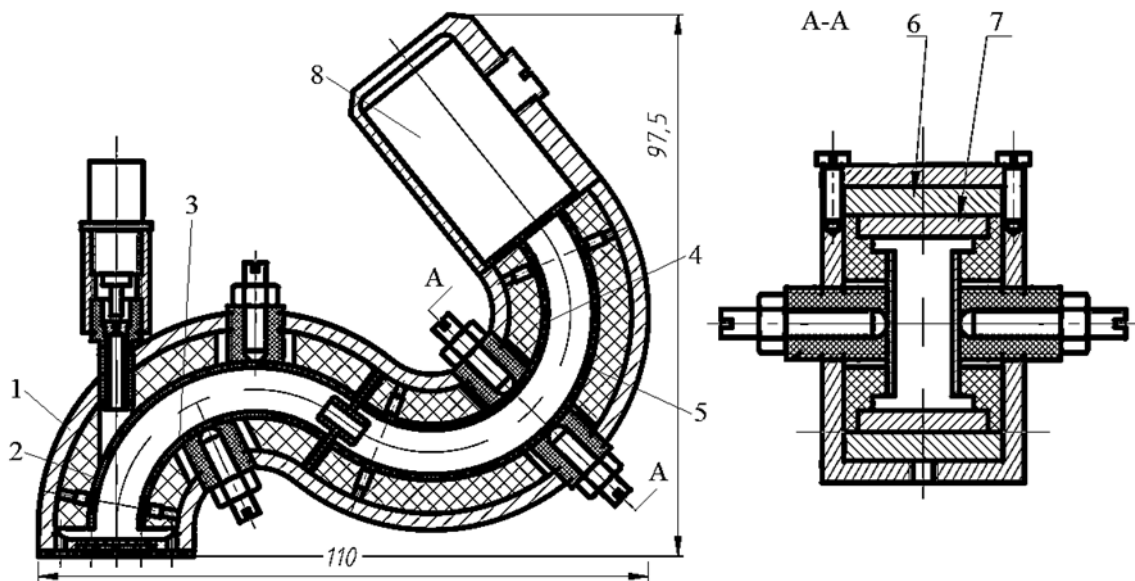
Эскиз сборочного чертежа гибридного анализатора: 1 – корпус; 2-5 – пластины конденсаторов; 6 – магнит; 7 – полюс; 8 – корпус ВЭУ-6-регистратора.
